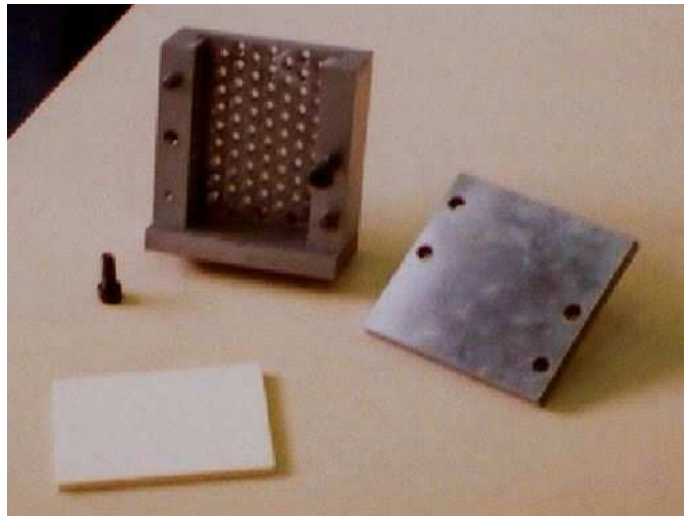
Moule conçu pour le coulage des éprouvettes d'essai.
